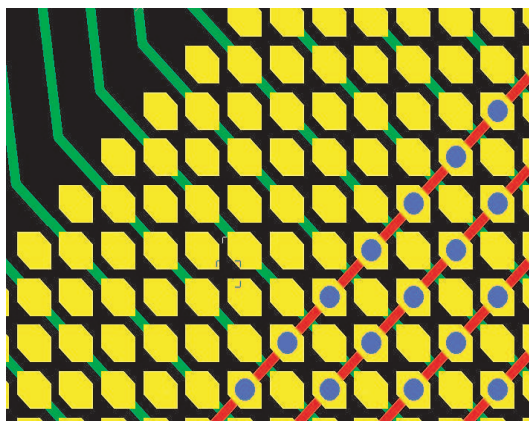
Schéma du plan de pistes bidimensionnel.
